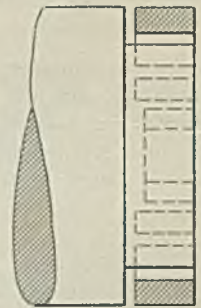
Abstechverfahren für zwei Laufringe der Kugellagerfabrik Schäfer & Co., Schweinfurt.
